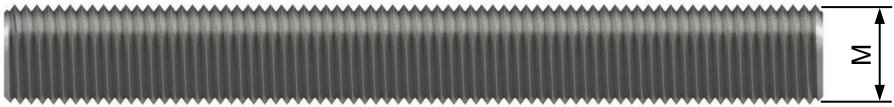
Gewindebolzen für Ankertypen G2, G3, G4 mit durchgehendem Gewinde
